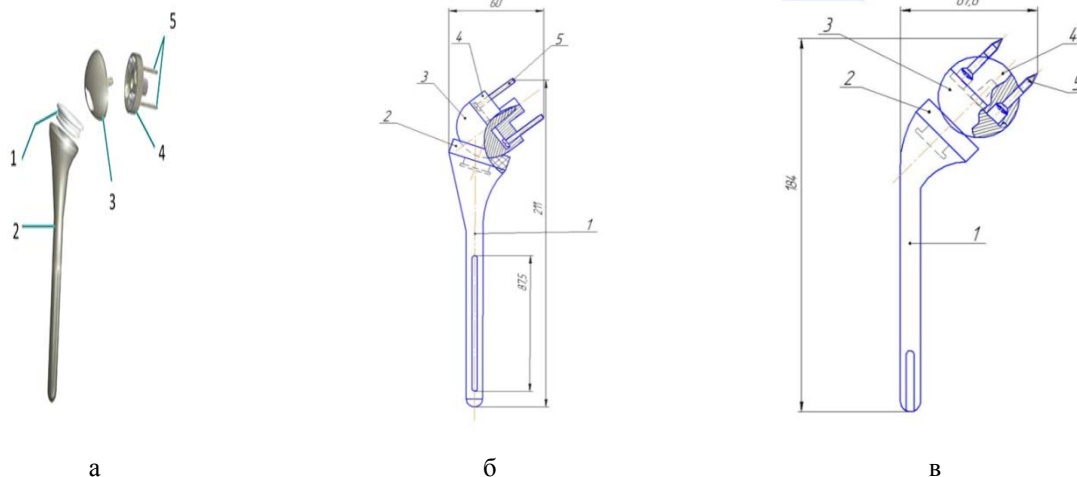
Схема прототипа (а) и сборочный чертеж (б), где: 1 - полиэтиленовый вкладыш, 2 -ножка, 3 - головка – гленосфера, 4 - основание, 5 -винты для крепления гленосферы к лопатке
